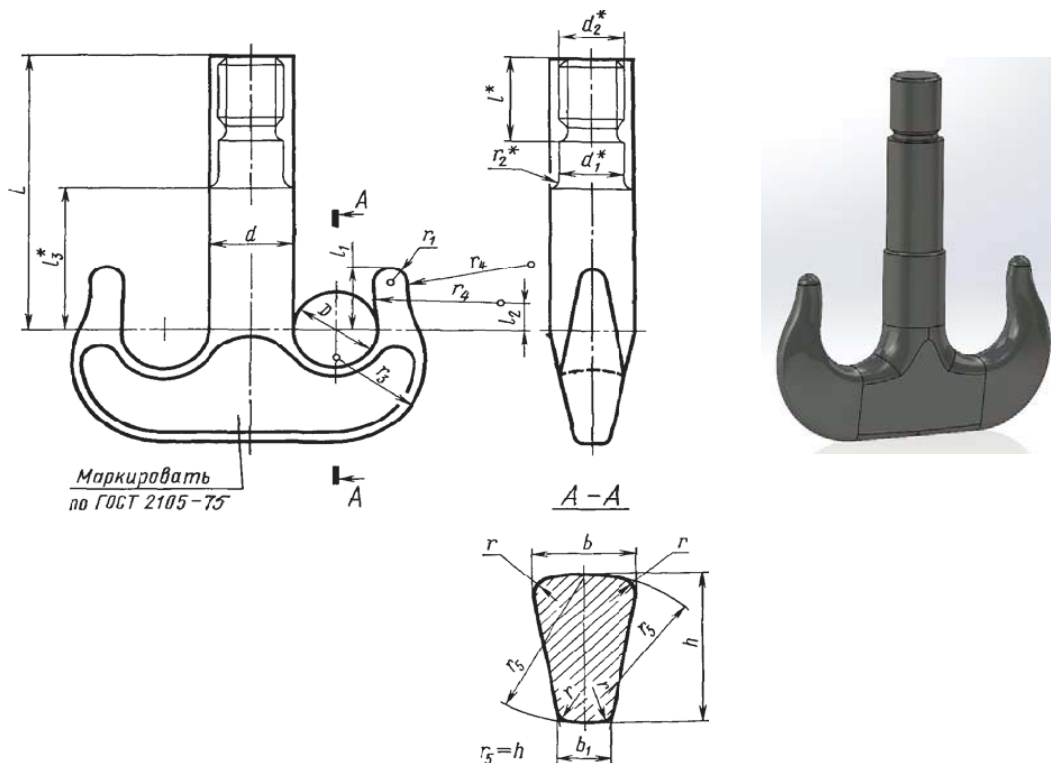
Конструкція і розміри моделі заготовки гака ГОСТ 6628-73
